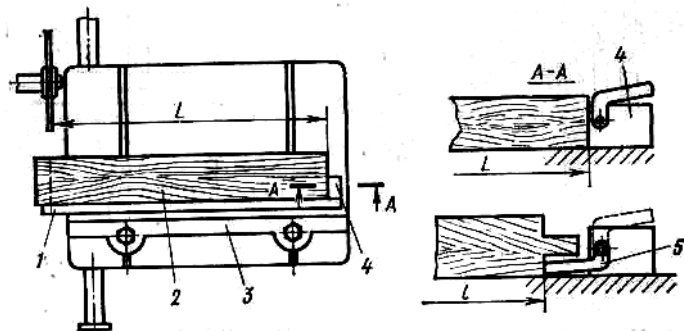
Установка торцевого упора на каретке шипорезного станка:
